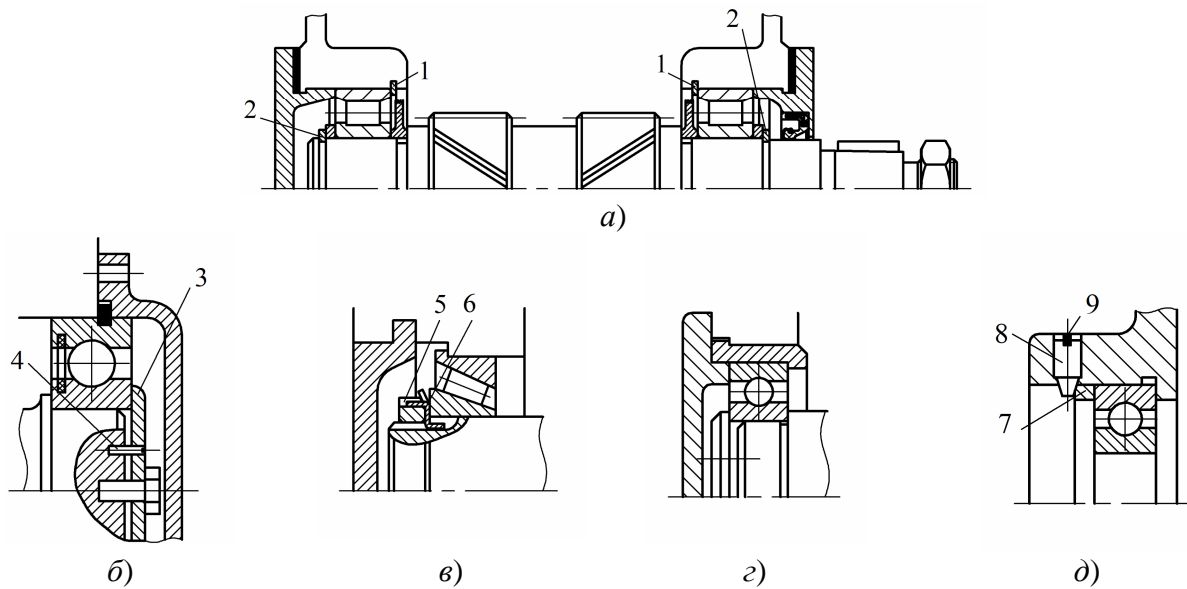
Схемы крепления подшипников в редукторах
